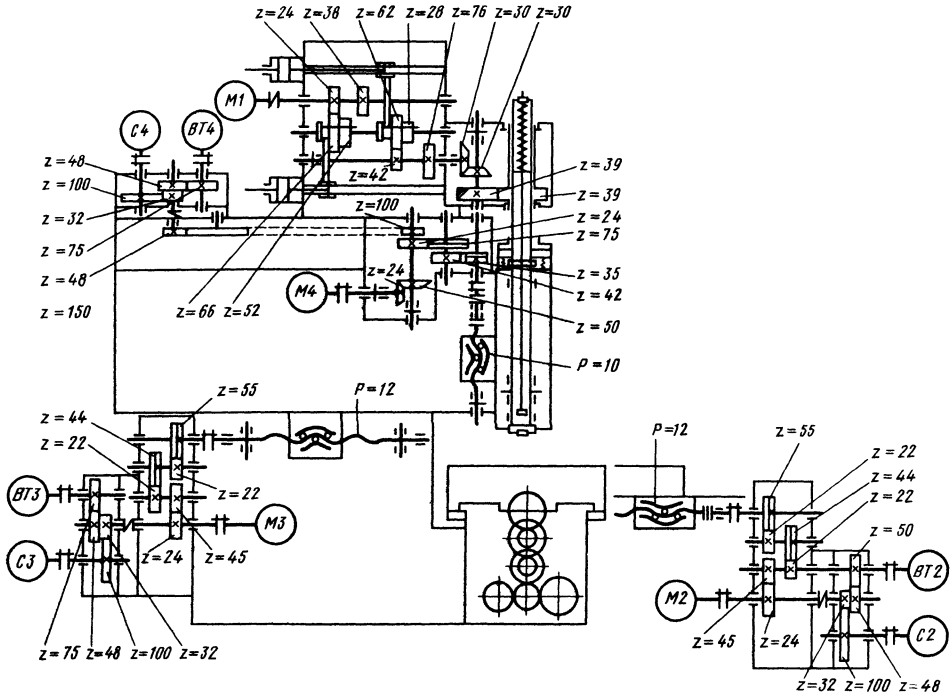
Кинематическая схема вертикально-фрезерного станка с ЧПУ
